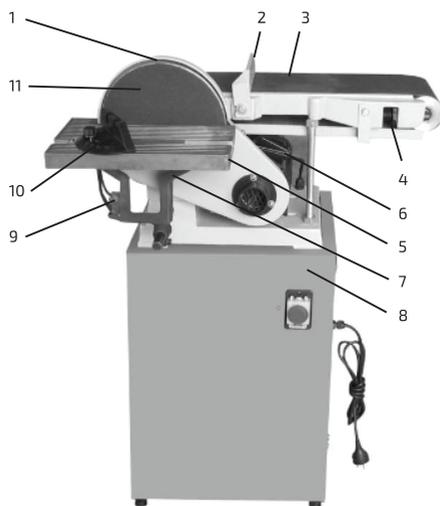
Устройство тарельчато ленточного-шлифовального станка
